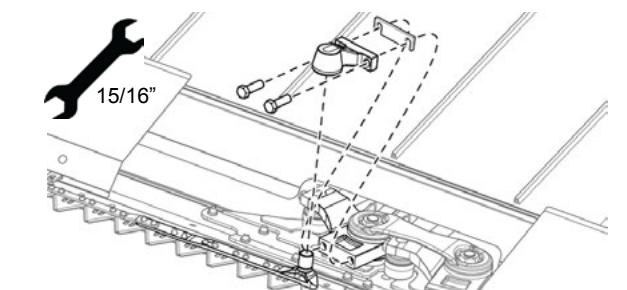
Снятие корпуса подшипников с головки правого ножа
